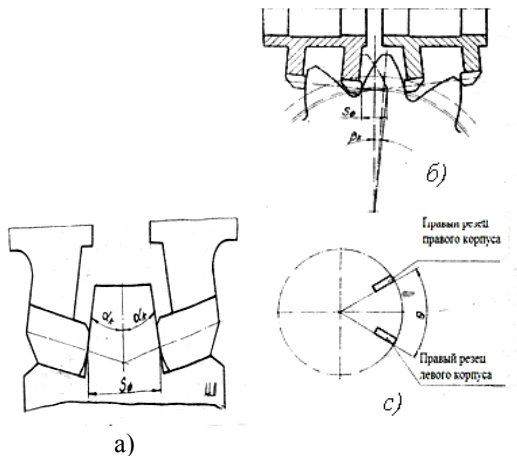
Установка и настройка фрезы а – шаблон для установки корпусов; б – поворот колеса на угол  $\beta$ ; с – разворот корпусов фрезы на угол  $\theta$
